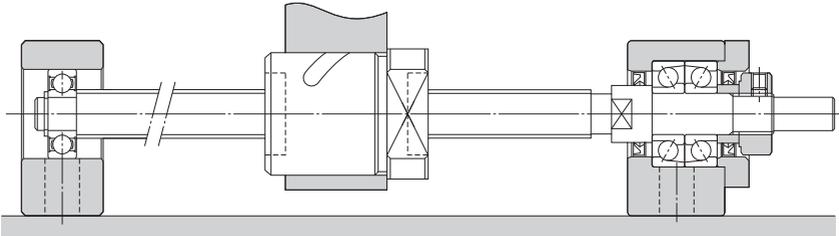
Пример установки концевой подшипниковой опоры прямоугольного типа
